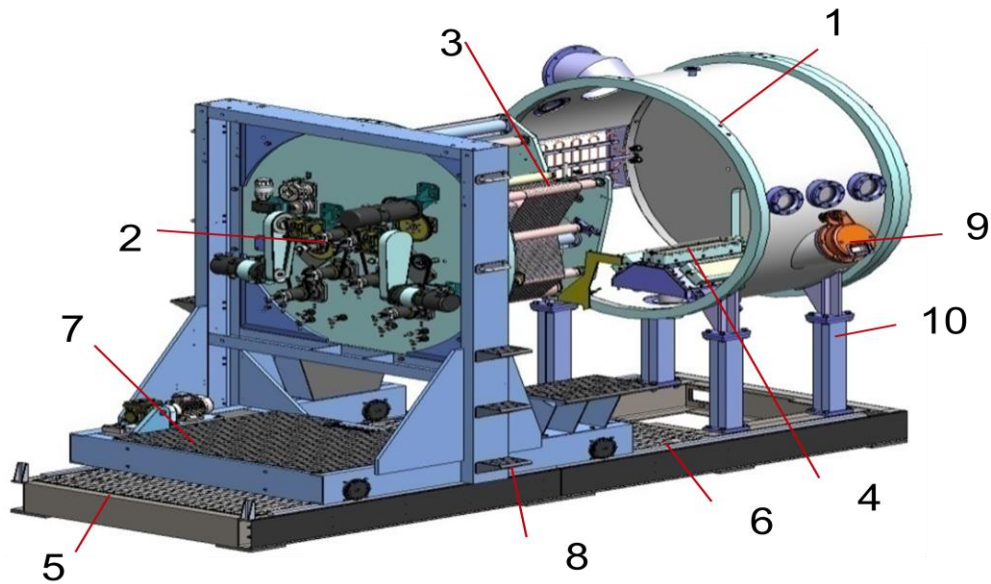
Устройство перемещения крышки вакуумной камеры
